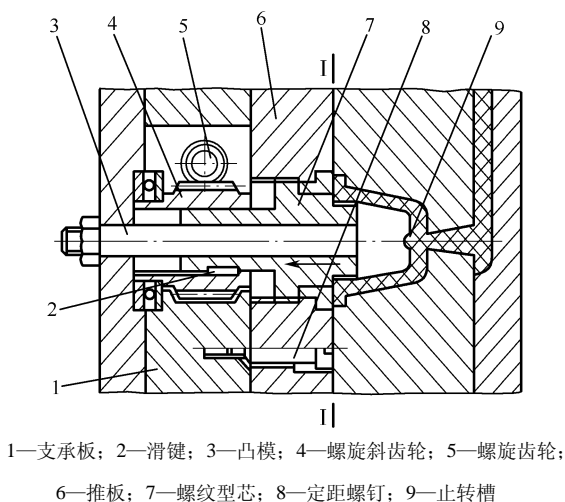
在模内装有斜齿轮手动脱卸内螺纹的模具结构
